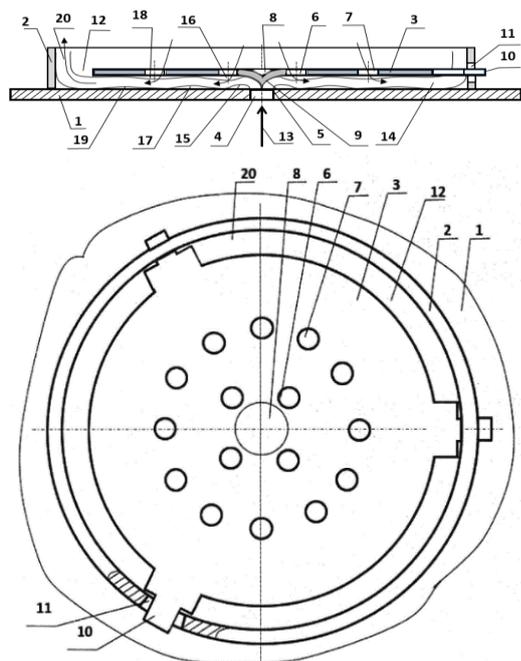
Колеблющийся жесткий или упругий клапан
